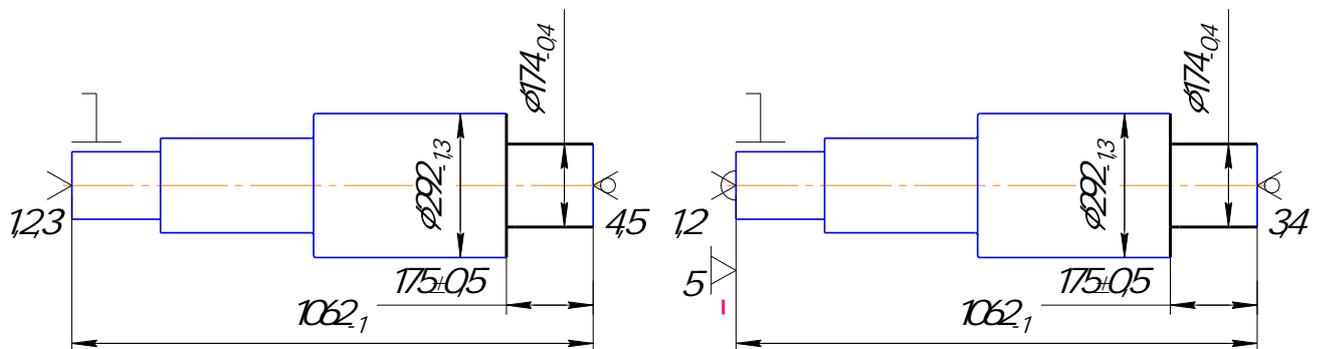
Варианты базирования детали при токарно-черновой обработке
